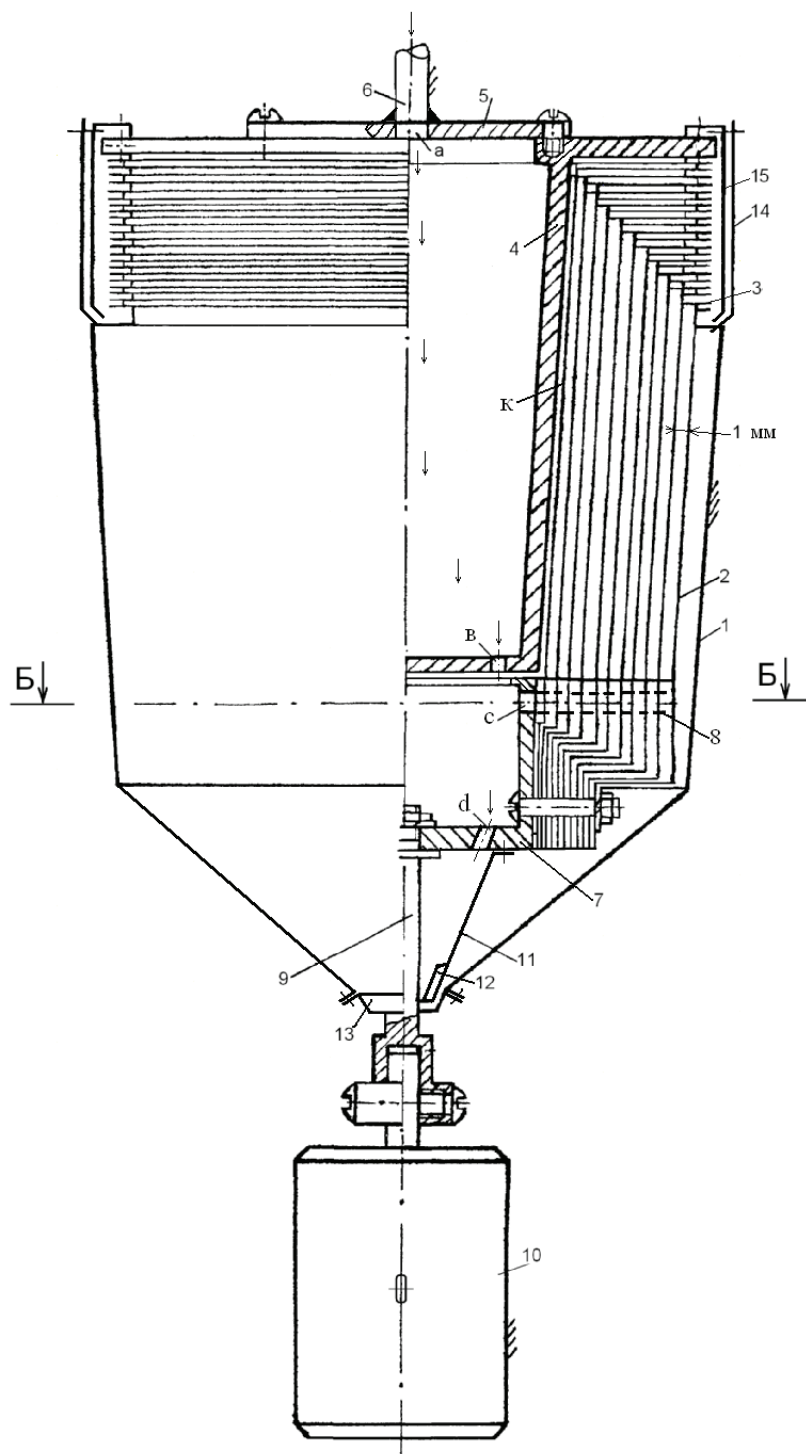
Монодисперсный распылитель жидкости: 1 — кожух; 2 — усеченный зубчатый конус; 3 — зубы распылительные, спаренные, двухрядные; 4 — неподвижный стакан; 5 — крышка; 6 — подводящий патрубок; 7 — вращающийся сосуд; 8 — насадки; 9 — приводной валик электродвигателя; 10 — электродвигатель; 11 — нижний усеченный конус; 12 — ускорительные лопатки; 13 — чашка; 14 — наружный отсечной щиток; 15 — внутренний отсечной щиток.
